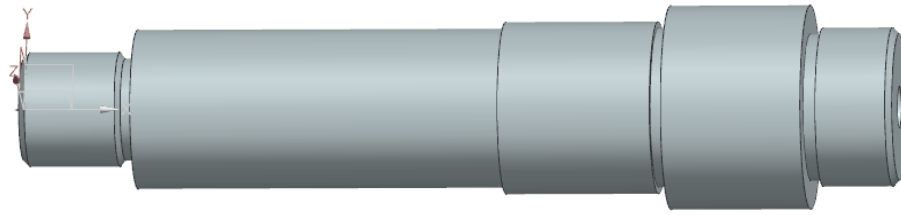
3D зображення заготовки (операція 025)
